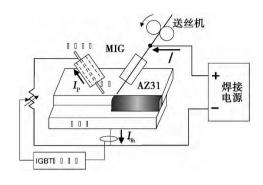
旁路分流 MIG 电弧熔钎焊工艺机理示意图 Fig. 1 Sketch for bypass-current MIG welding-brazing
